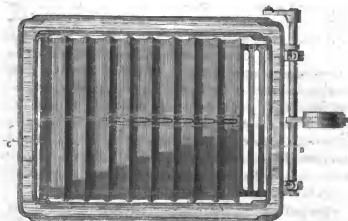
Plan d'un foyer à grille Chobrzynsky.
